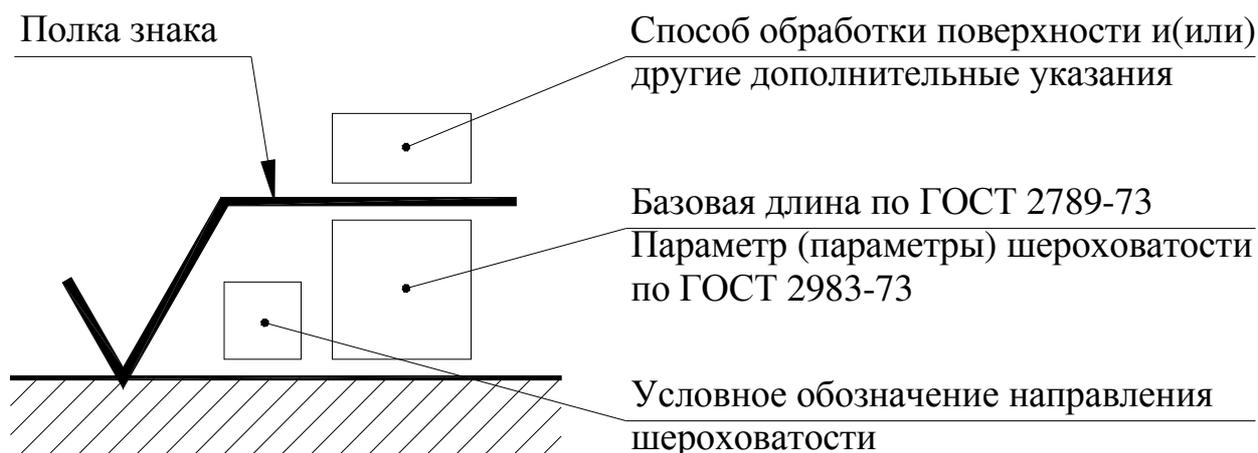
Структура обозначений шероховатости поверхности
